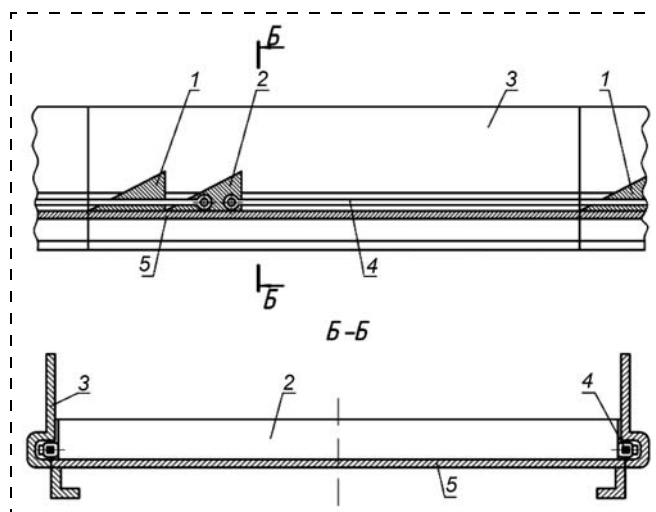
Конструкция клинового перегружателя скользящего типа: 1 — неподвижный транспортирующий элемент; 2 — подвижный транспортирующий элемент; 3 — борт; 4 — тяги; 5 — днище
